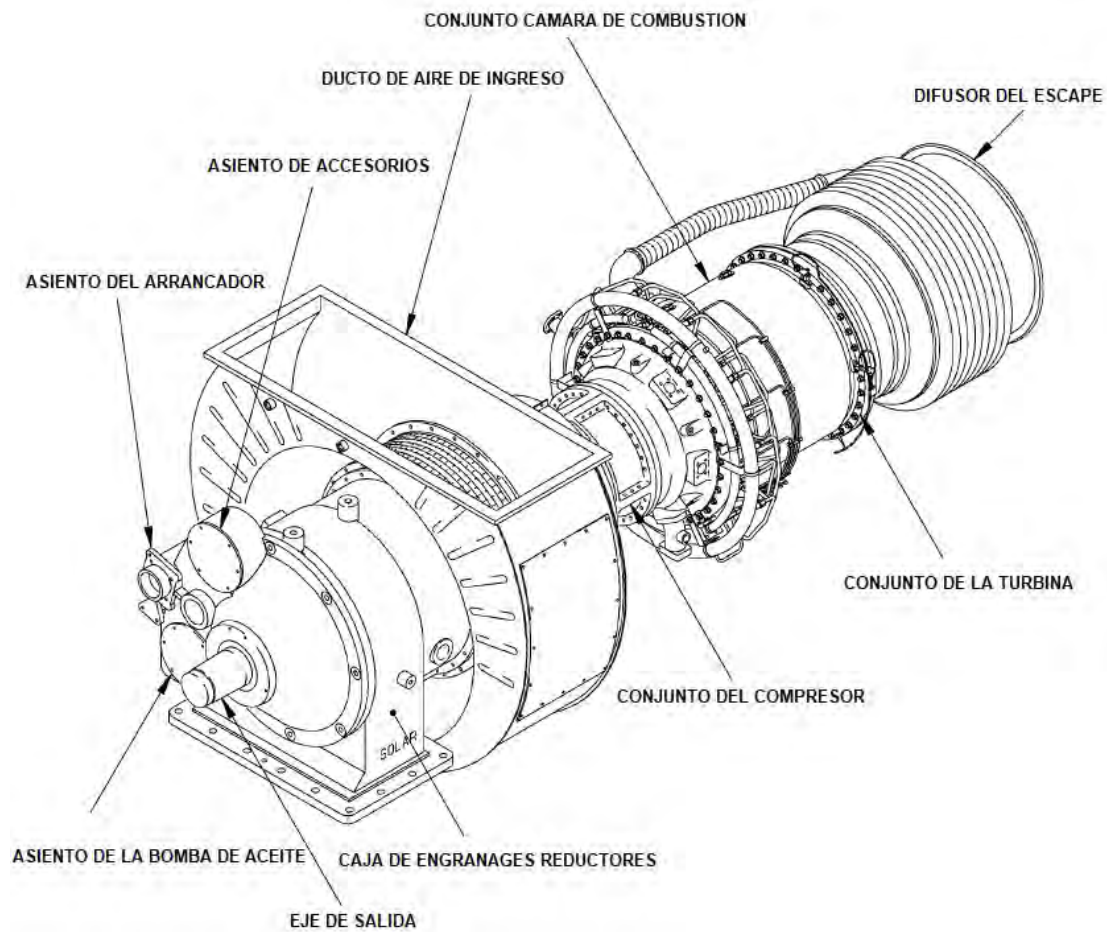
Partes principales de la turbina Centaur 50 [71].
